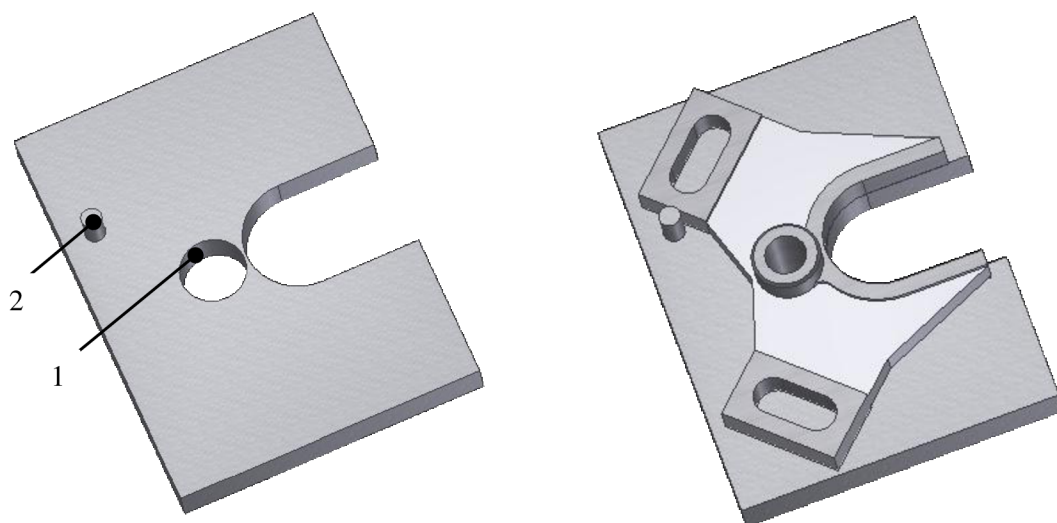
Model přípravku pro přerušované soustružení čela
